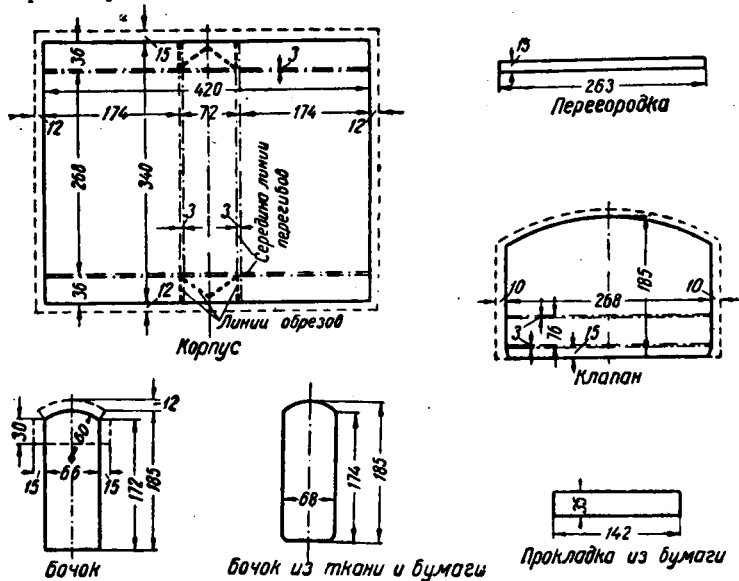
Чертеж деталей сумки и ранца размером 32 × 23 × 8 см
